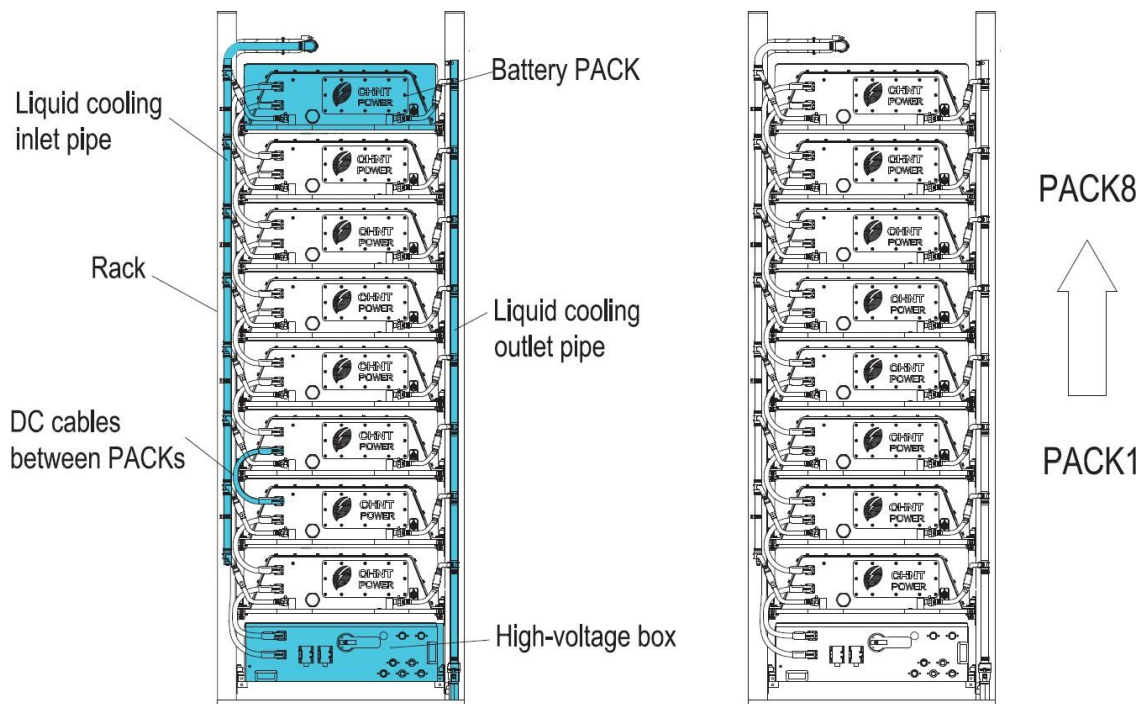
Diagrama esquemático de la conexión del conjunto de baterías
